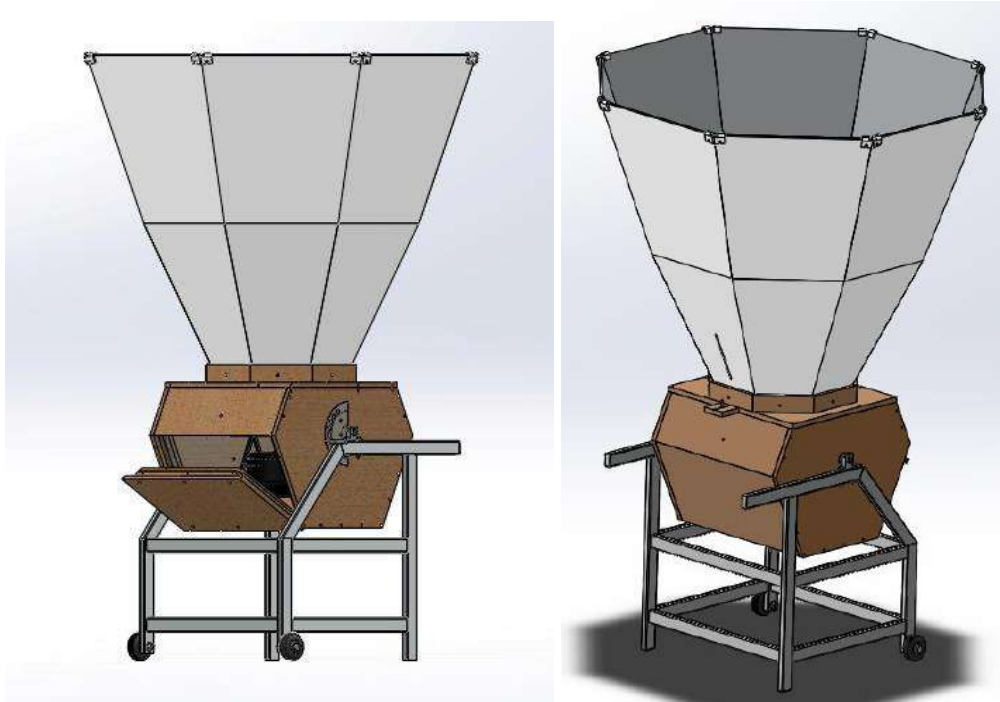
Diseño CAD definitivo del prototipo de cocina solar
